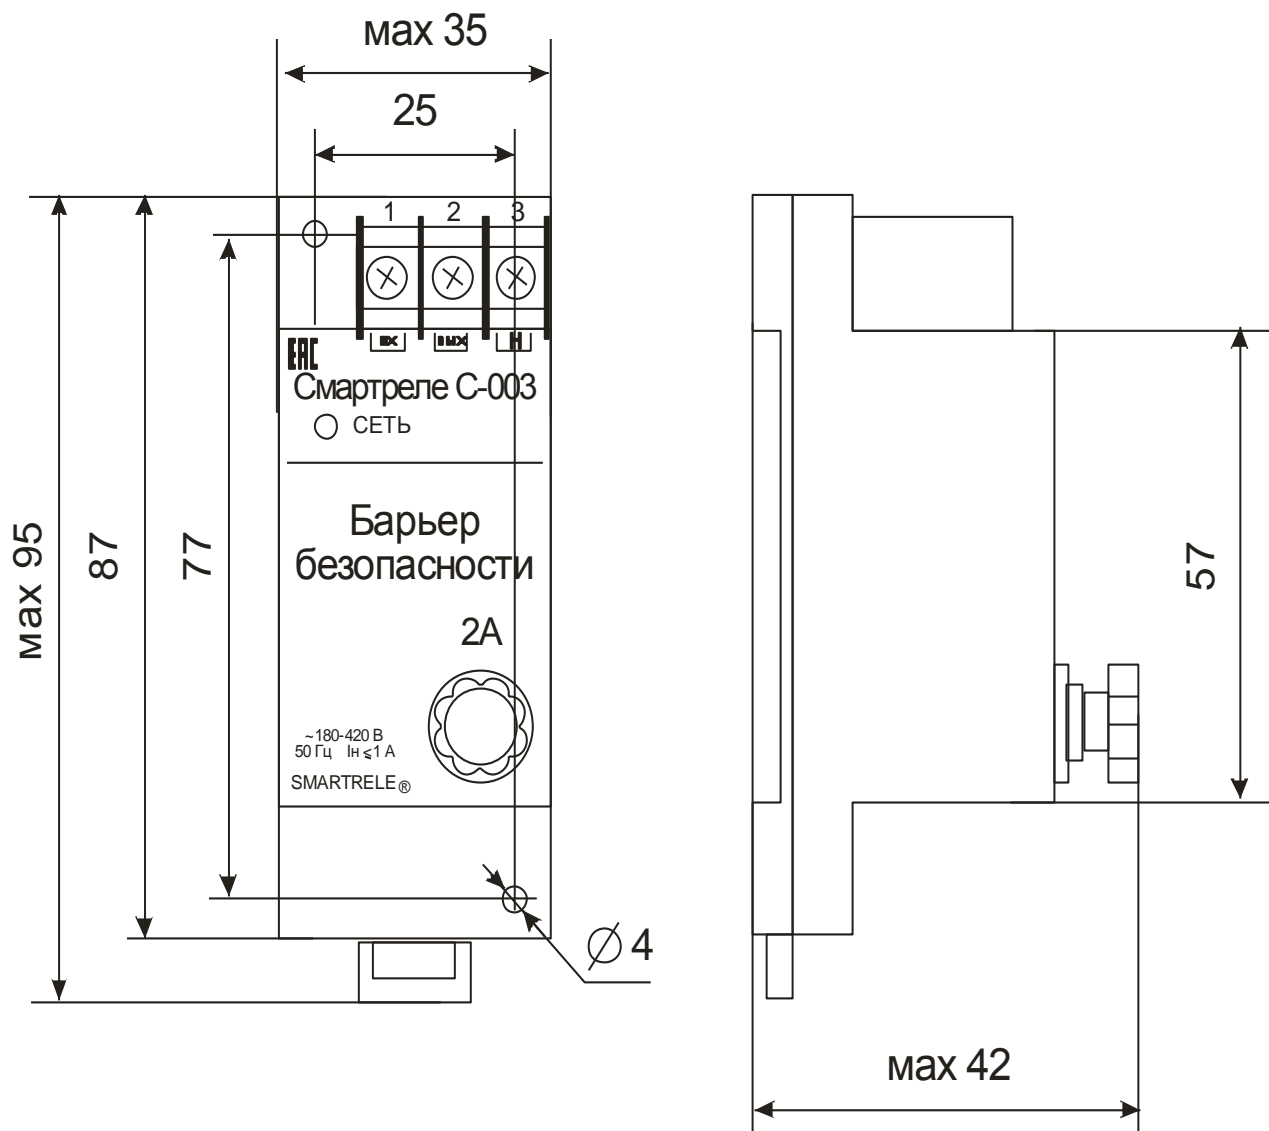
внешний вид, габаритные и установочные размеры Смартреле С-003
